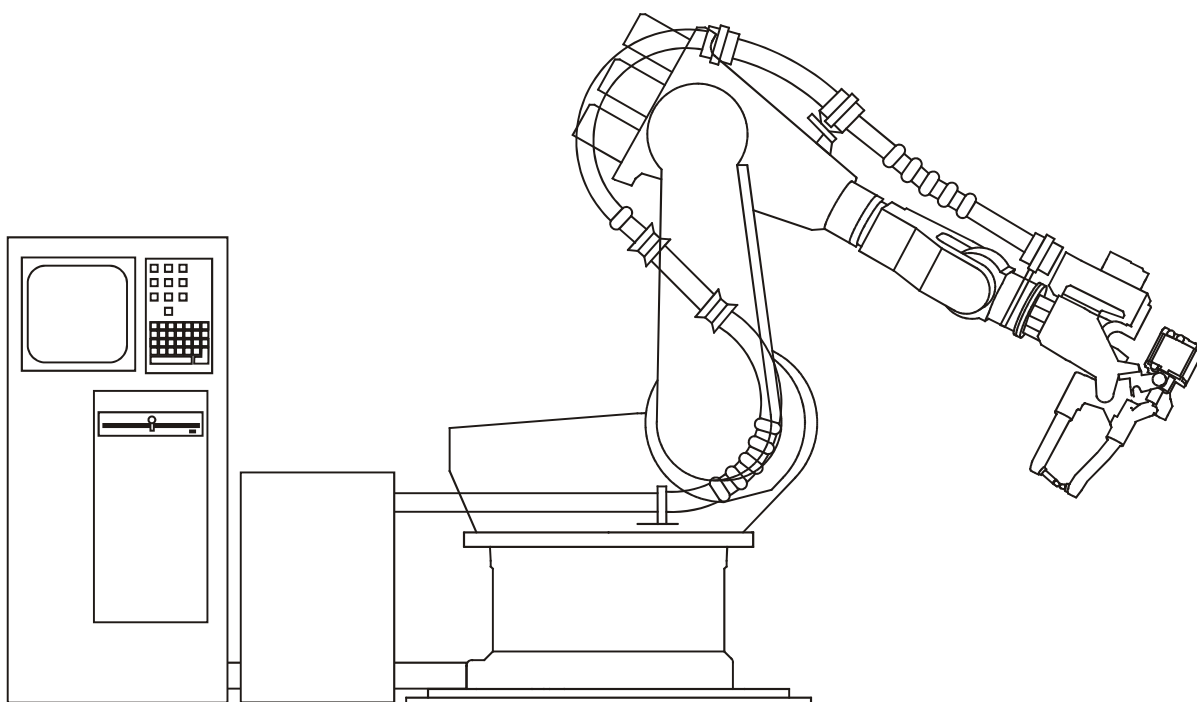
Использование промышленного сварочного робота при контактной точечной сварке
